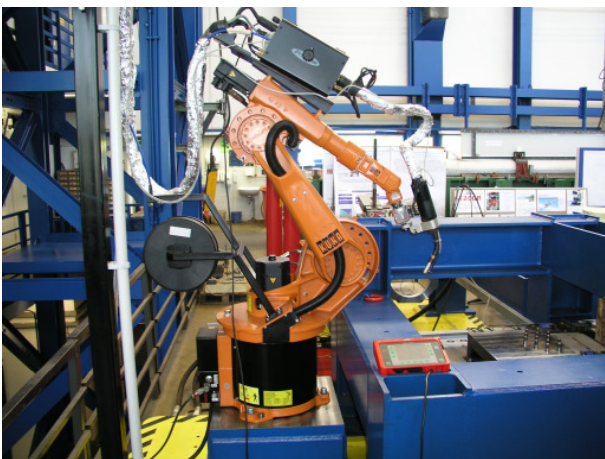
Schweißroboter KR6 mit Push-Pull-Einheit
